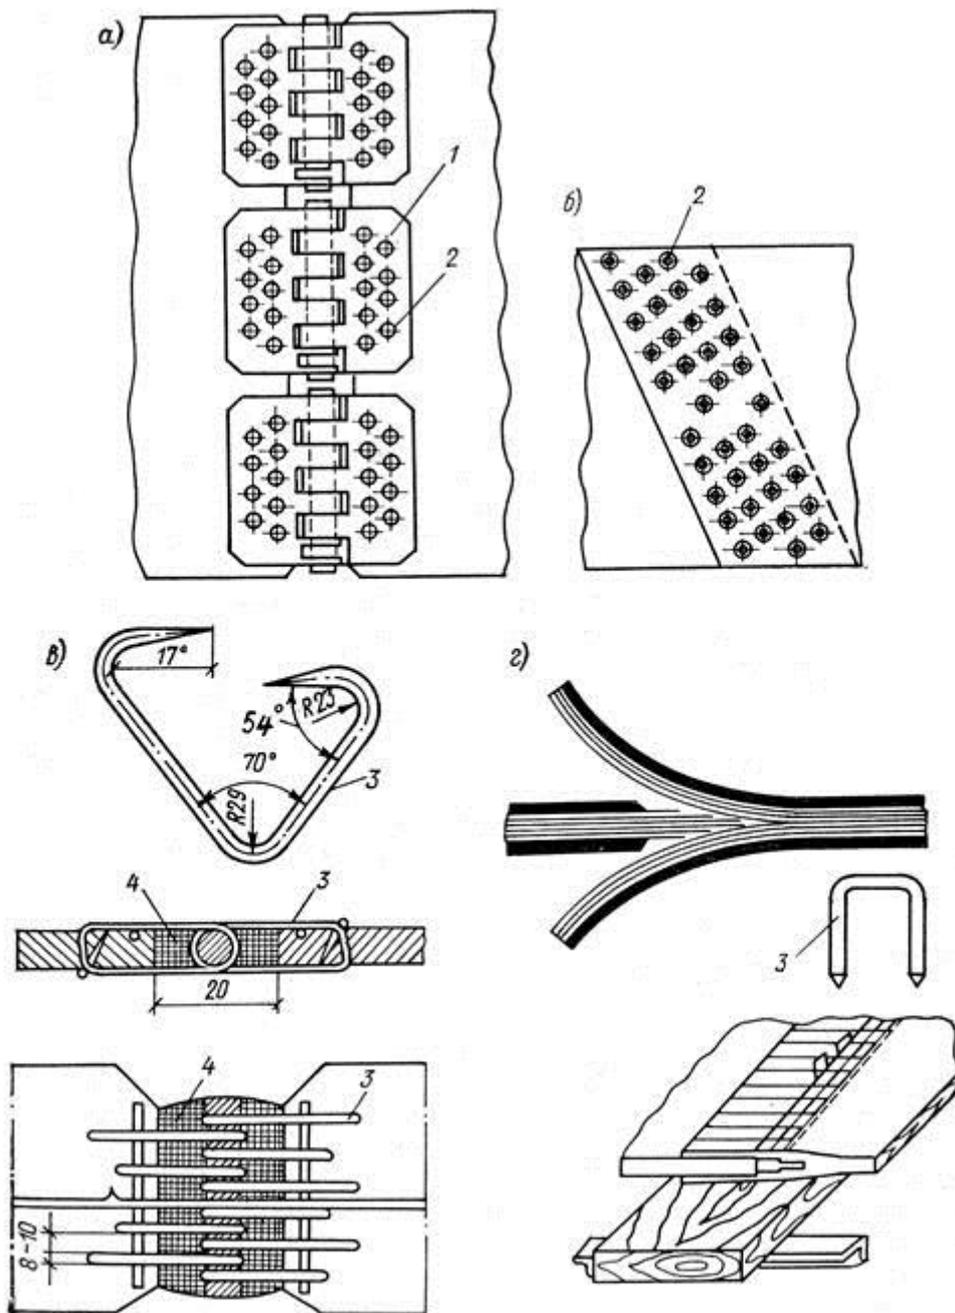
Стыковка лент механическими средствами: а – шарнирами; б – заклепками; в – крючкообразными скобами с канатом; г – П-образными скобами; 1 – петля; 2 – заклепка; 3 – скобы; 4 – уплотнительный шнур
